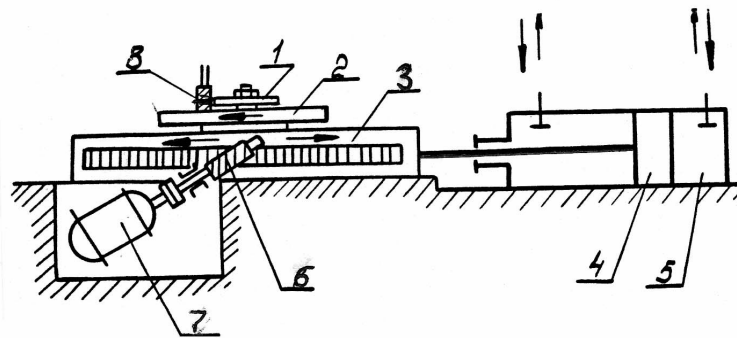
Схема приводу подачі копіювально-фрезерного верстата
